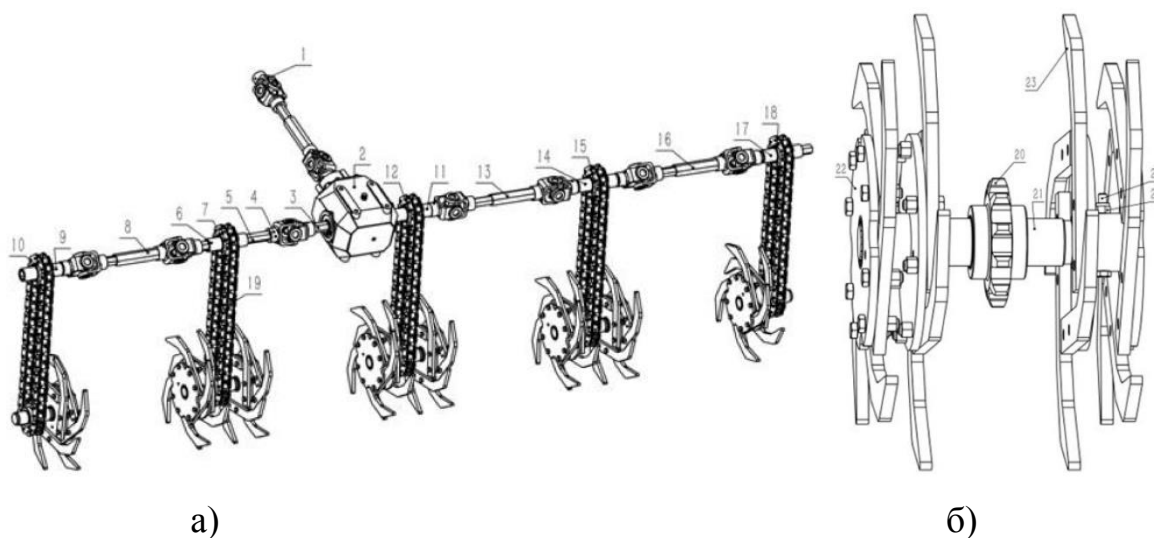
Схема почвообрабатывающей фрезы для обработки посадок картофеля: а - схема привода; б - общий вид рабочих органов.
